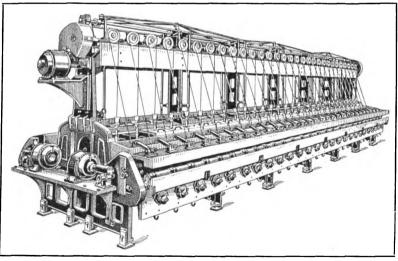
Kunstseide-Spinnmaschine mit elektr. Zentrifugen und Einzelantrieb der Hauptwellen (Spinnzentrifugen-Schalter älterer Ausführung).
